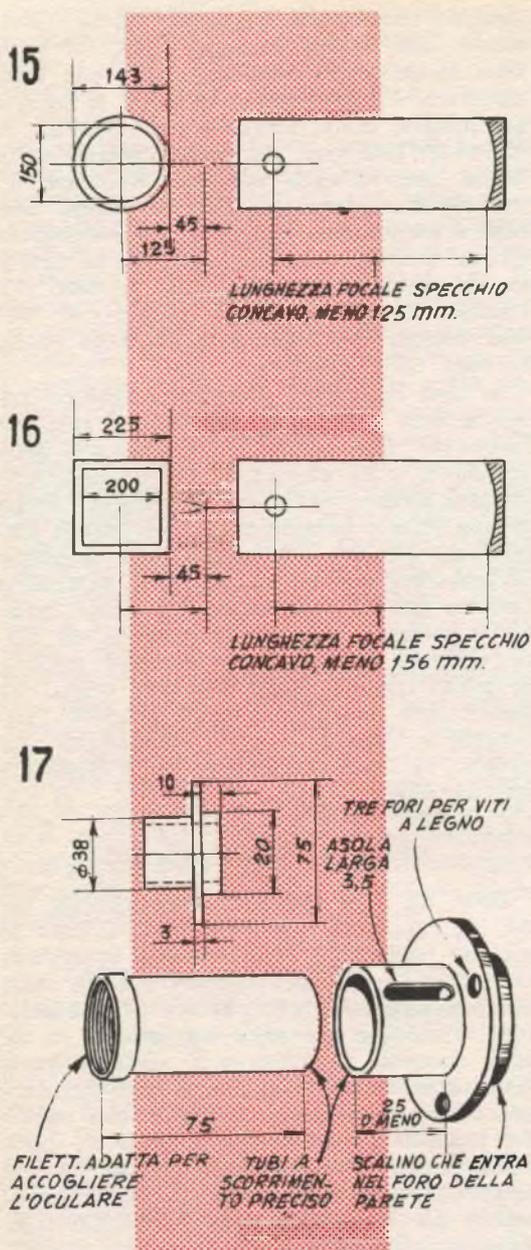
Posizione con approssimazione del foro dell'oculare in un telescopio con tubo a sezione circolare. FIG. 16) - Posizione con approssimazione del foro per l'oculare, in un telescopio con tubo o struttura a sezione quadrata. FIG. 17) - Dettagli complesso portaoculare con sistema di scorrimento per messa a fuoco.
